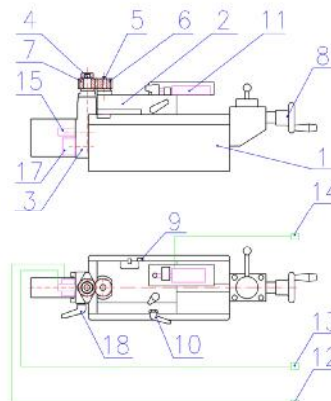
Основные части прибора зубоизмерительного GearSpect DO-0 PC
